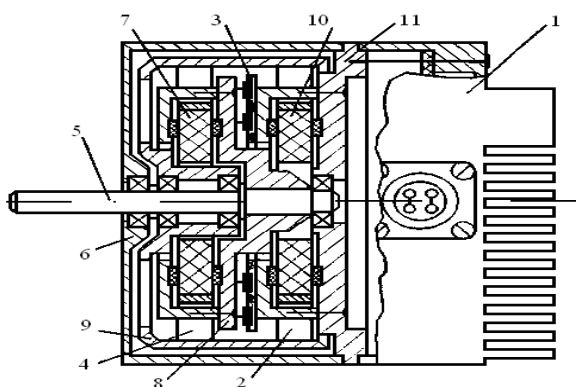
Конструктивне виконання двигуна реверсивного обертання:
